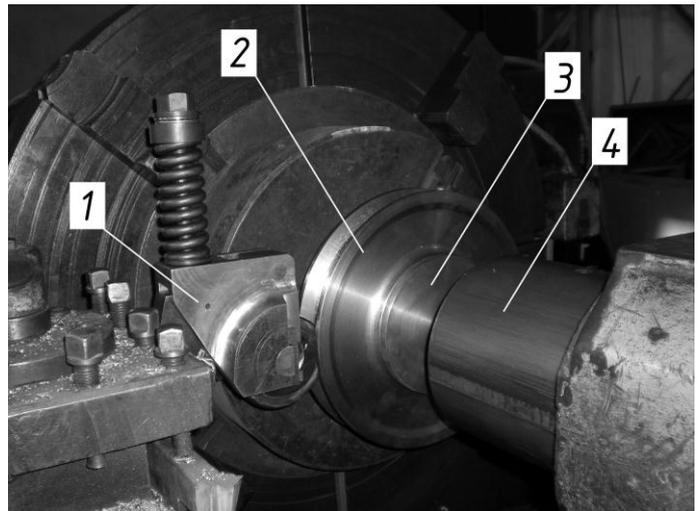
Общий вид экспериментального оборудования: 1 – устройство для обкатывания канатных блоков; 2 – канатный блок; 3 – оправка; 4 – задняя бабка токарного станка
